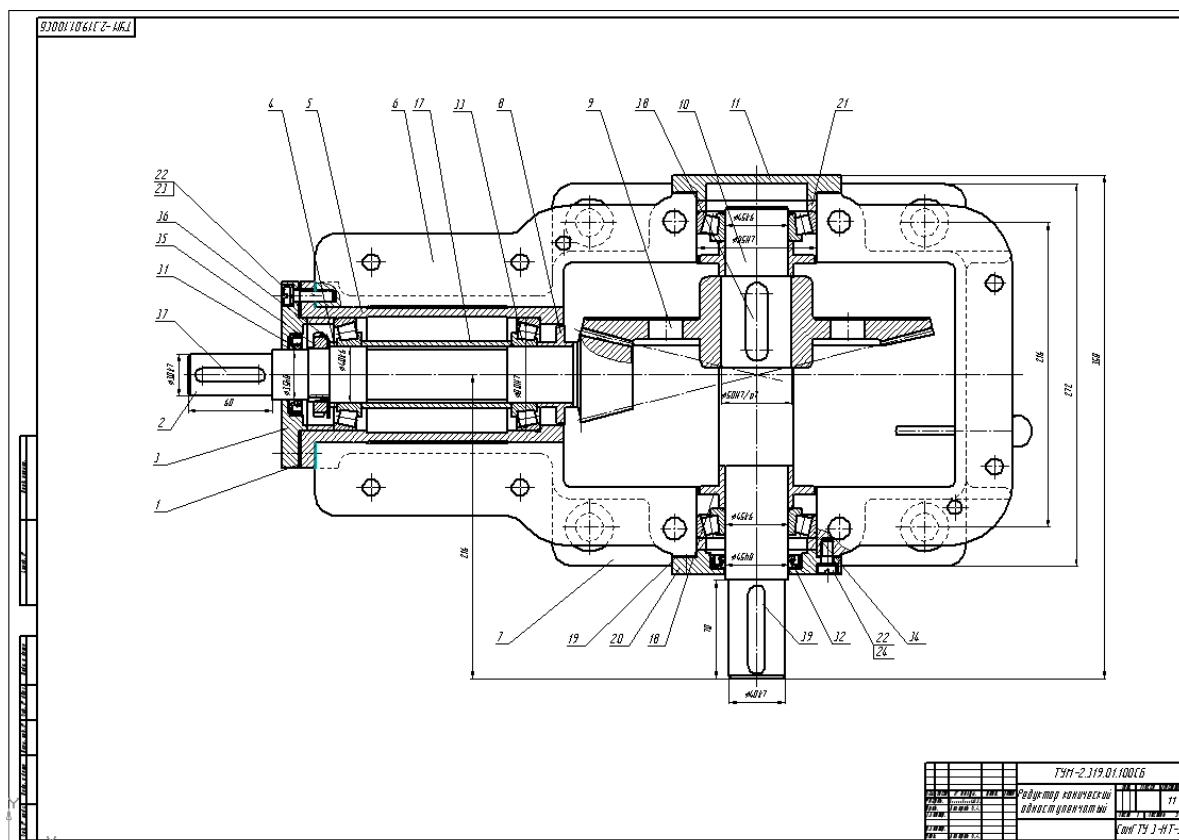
Пример сборочного чертежа конического редуктора (вид сверху без крышки)
